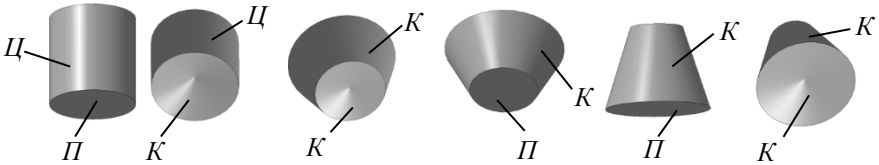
Поверхні, що обмежують тіло фрези
